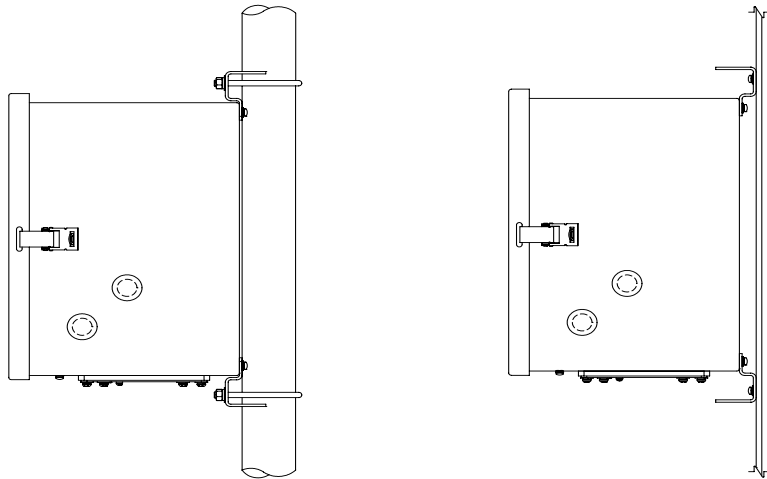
(Montaje del 6270 OEU en tubería o panel)
